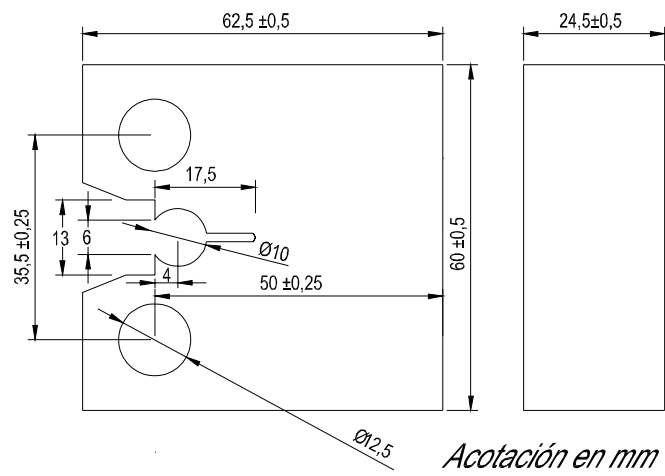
Dimensiones de la probeta compacta de tensión estándar
